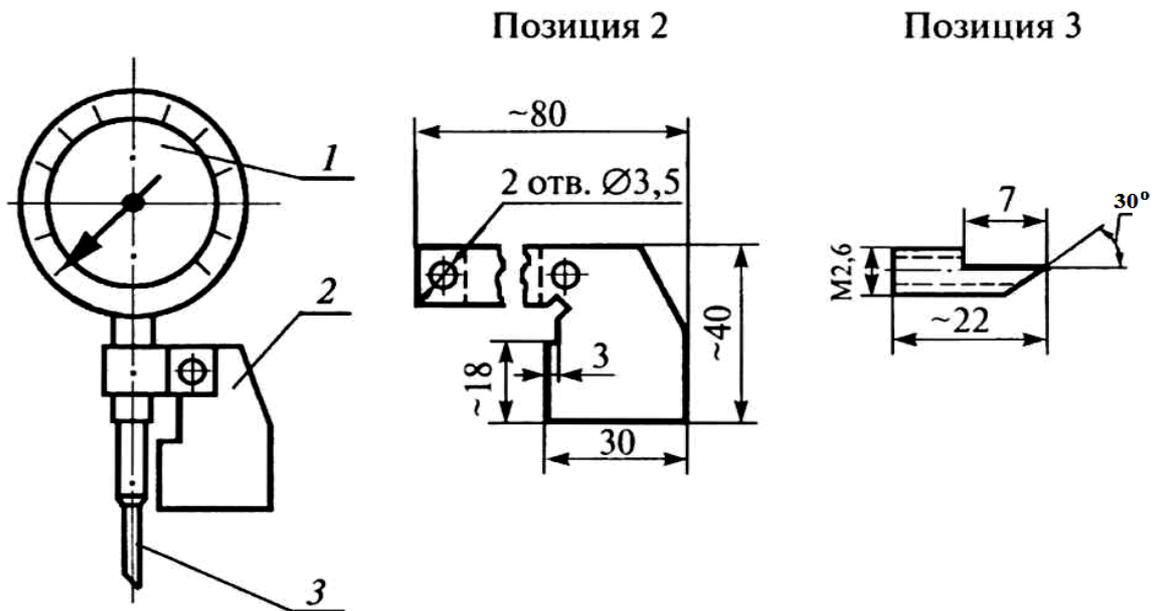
Приспособление для измерения глубины подрезов: 1 – индикатор «0–10» с поворотной шкалой; 2 – опорный кронштейн; 3 – измерительная игла
